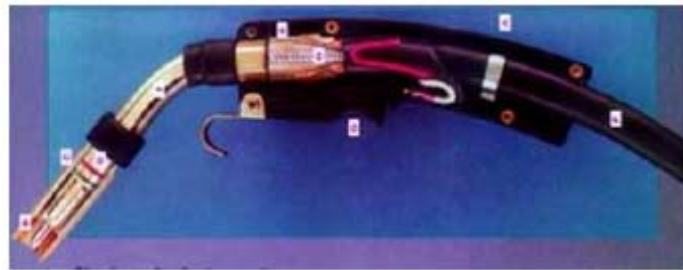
Pistola per a soldadura metàl·lica amb arc i gas.
